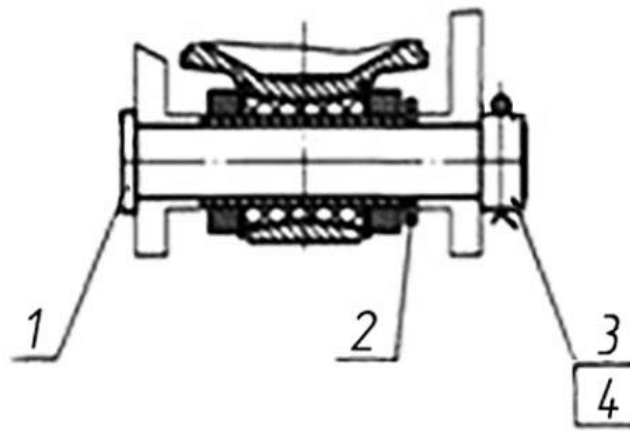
Резинометаллический пакет продольного поводка конструкции ТВЗ
